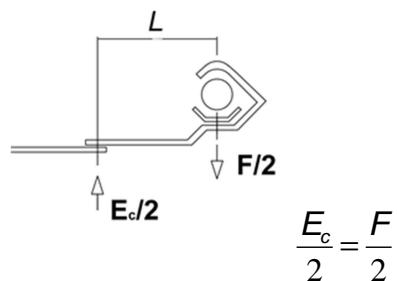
Vista superior abrazadera. Fuerzas desplazamiento recto.
